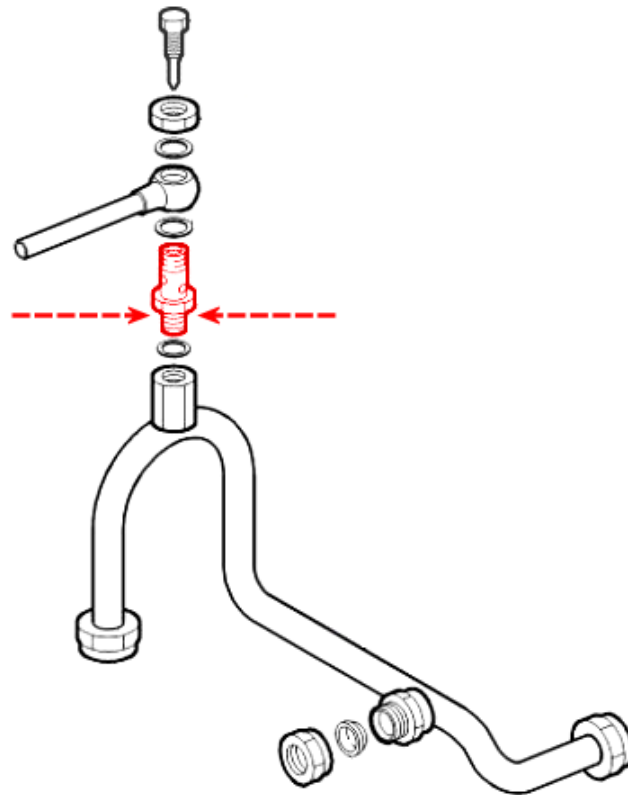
Válvula de purga de combustible del motor MTU 16V 4000 M70.
